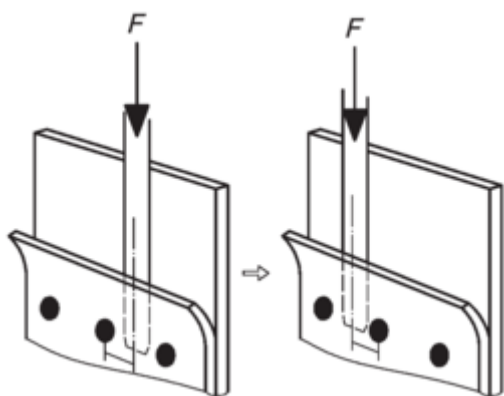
Zkouška odlupem – mechanické provedení [26].
